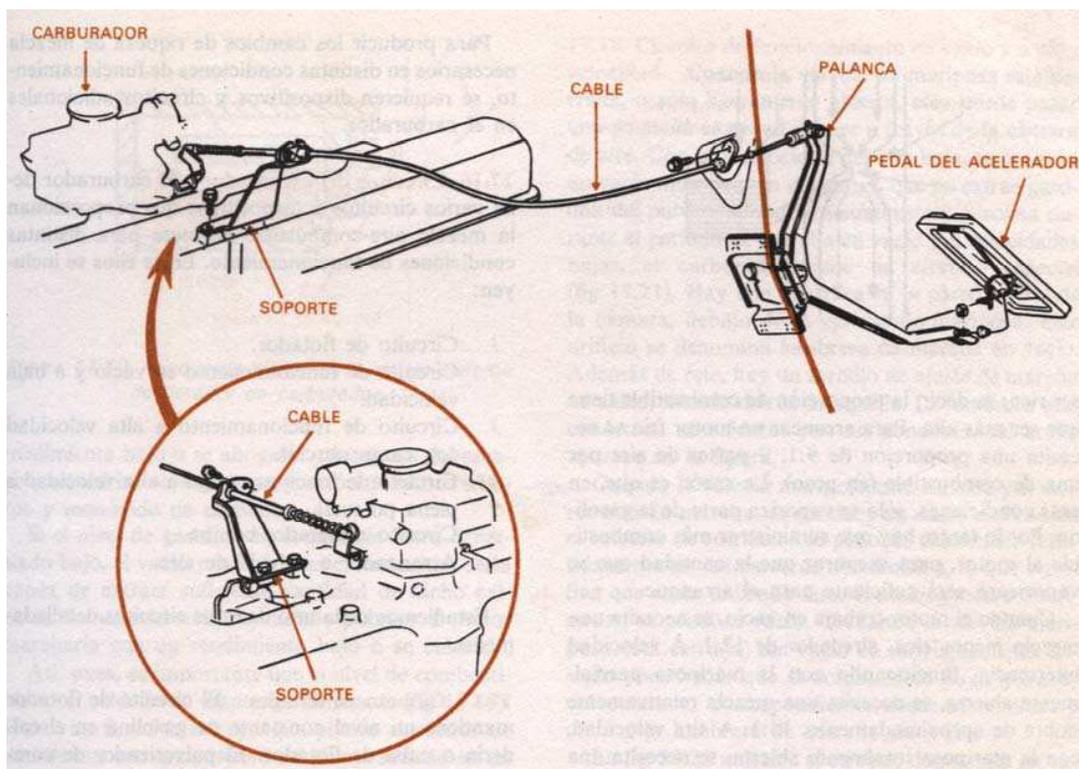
Enlace pedal del acelerador - válvula mariposa en el carburador.
